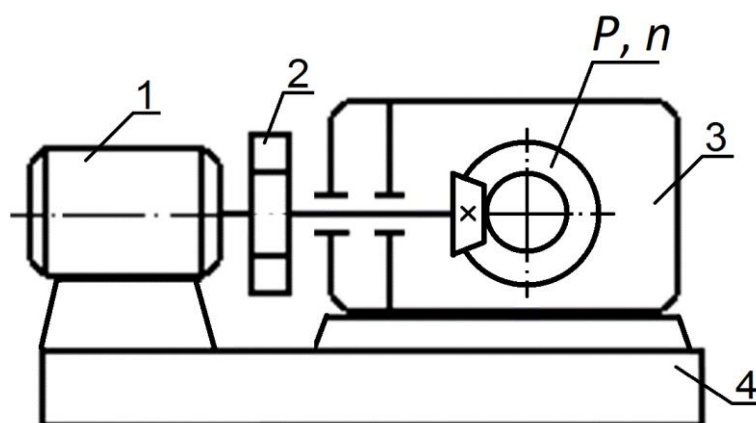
Привод ковшового элеватора: 1 – электродвигатель; 2 – горизонтальная клиноременная передача; 3 – одноступенчатый конический редуктор; 4 – литая плита
